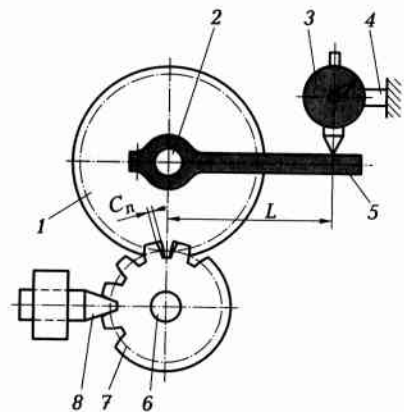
Схема измерения бокового зазора в цилиндрической зубчатой передаче:
